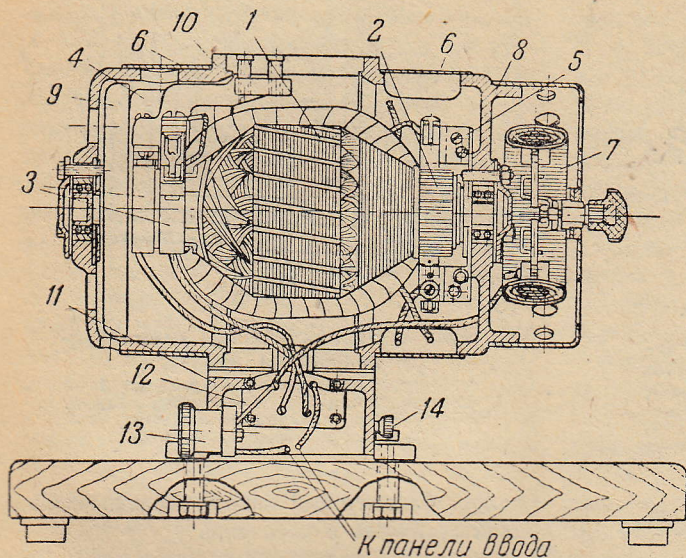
Конструктивная схема преобразователя Одесского завода Кинап
